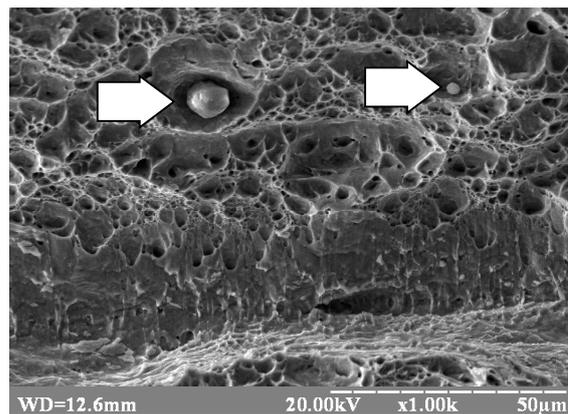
Поверхность разрушения низкоуглеродистой стали [13] / Fig. 5. The fracture surfaces of low-carbon steel [13]
